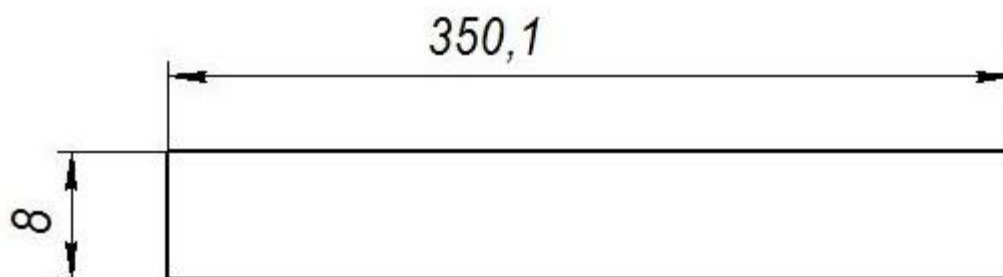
Эскиз обрабатываемой поверхности предварительным фрезерованием.
